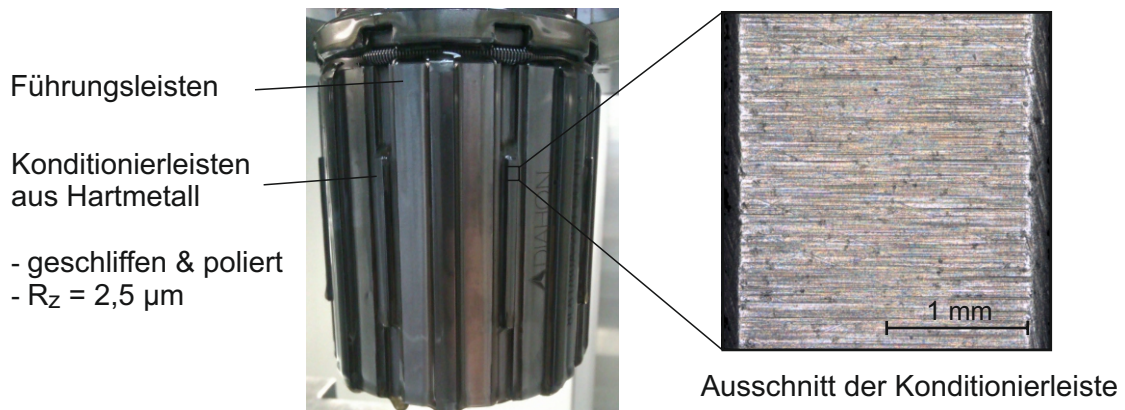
Konditionierwerkzeug auf Basis eines Honwerkzeuges mit eingesetzten Konditionierleisten
